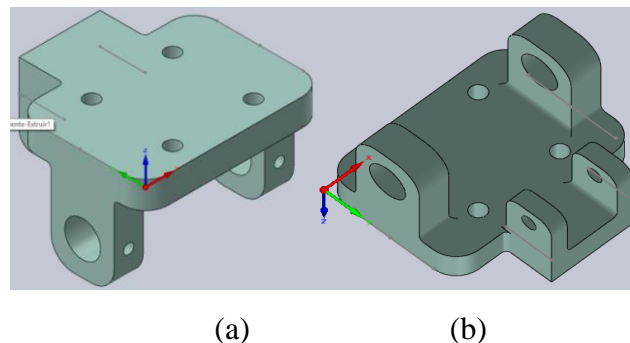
Diseño de la parte móvil (a) Vista superior, (b) Vista inferior.
